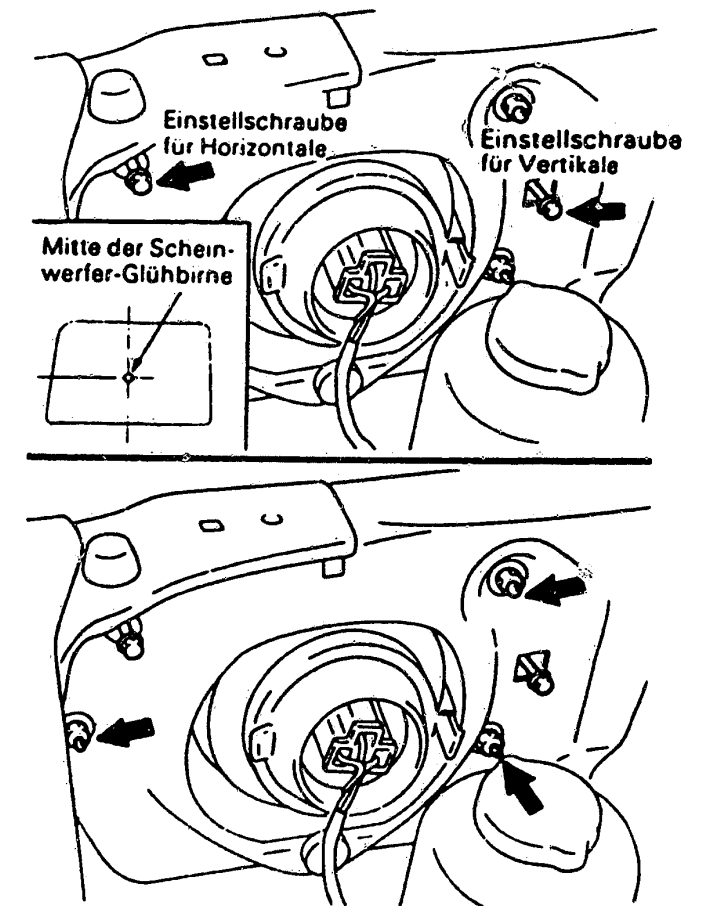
Einstell- und Befestigungsschrauben der Frontscheinwerfer, vom Motorraum aus gesehen.
